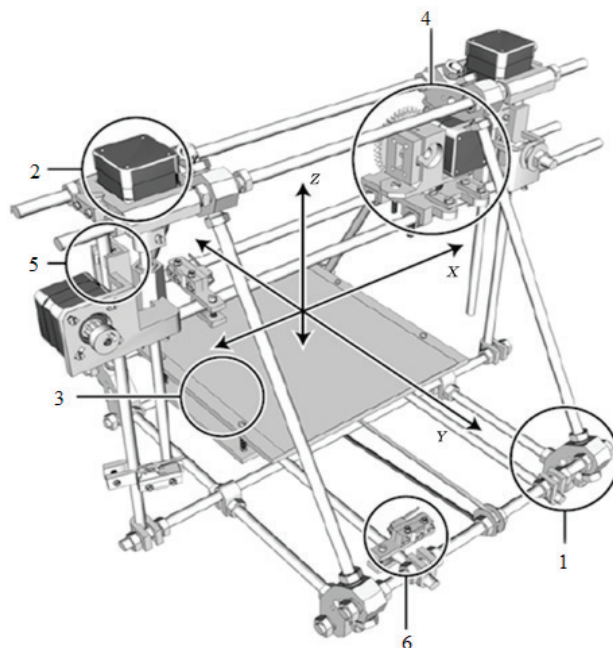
Трехмерный принтер Prusa Mendel. 1 — рама, 2 — шаговый двигатель, 3 — подложка, 4 — экструдер, 5 — направляющие, 6 — концевые выключатели
